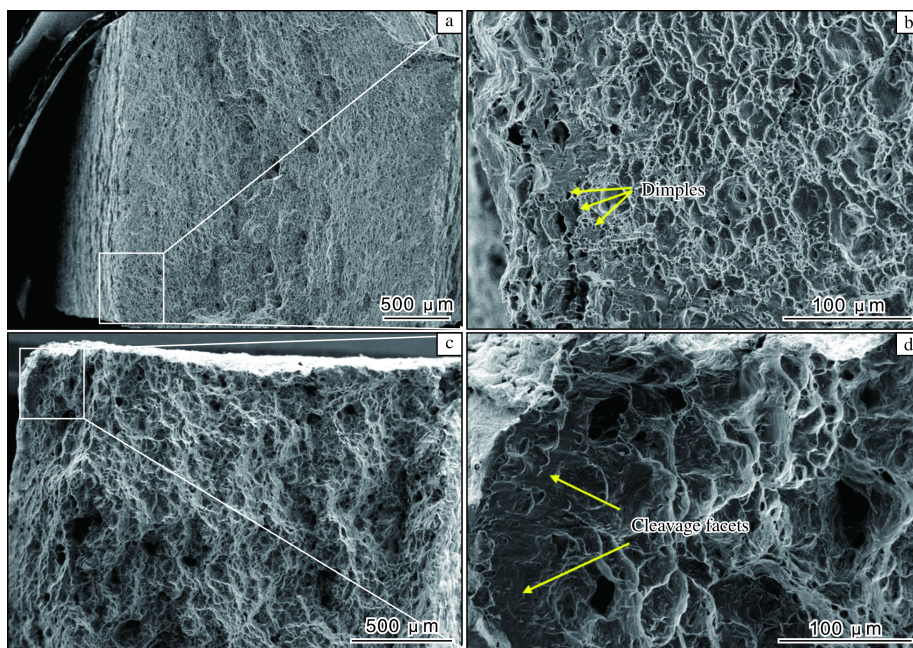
Zr702 合金焊接接头在不同环境中慢速率拉伸试样的断口形貌
